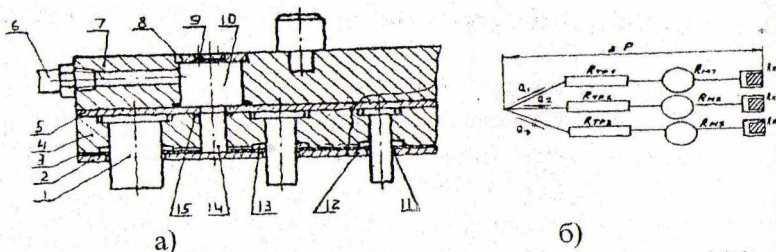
Вирубний штамп з внутрішнім резервуаром (а) і схема маслопроводу штампу (б)
